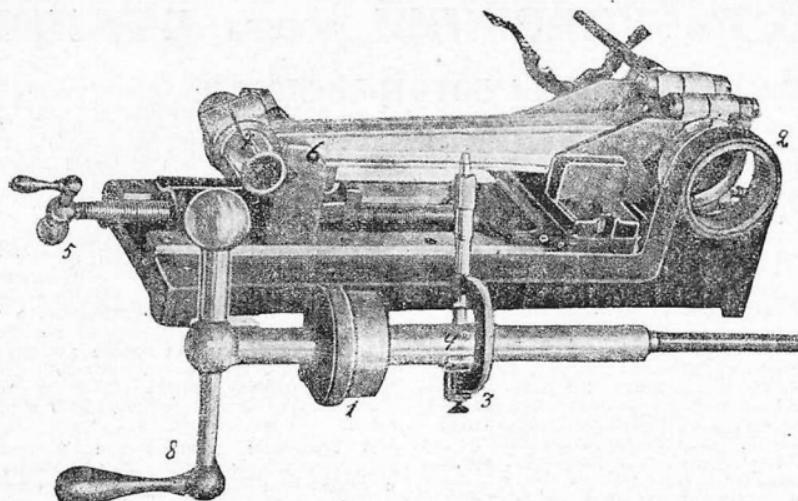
Приспособление дает возможность обработки и шатунных подшипников
